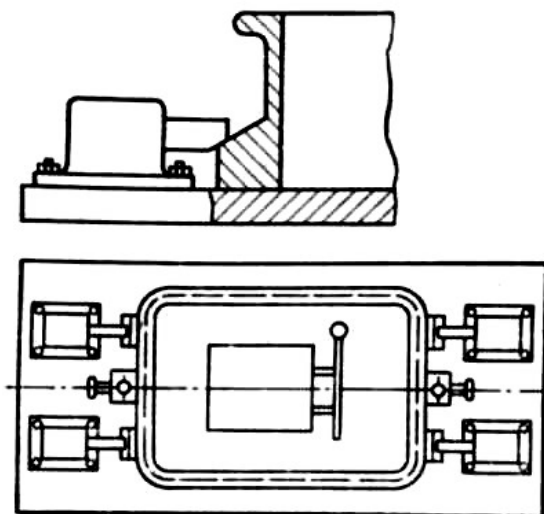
Пневматическое закрепление опок на столе формовочной машины
